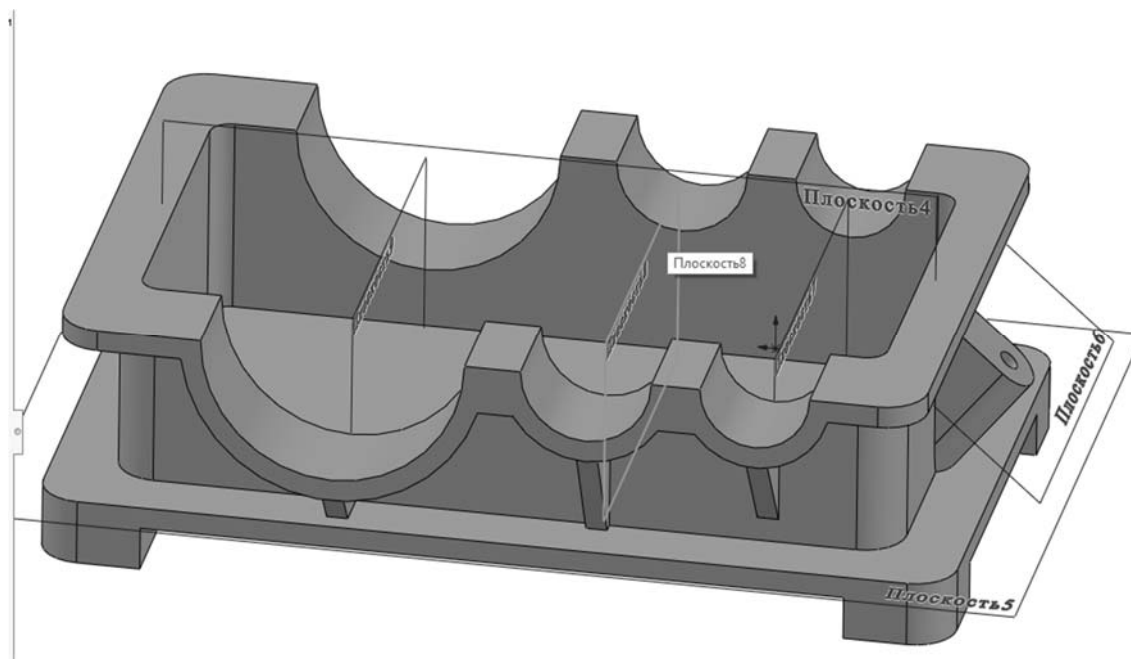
Изображение 3D-модели корпуса редуктора
